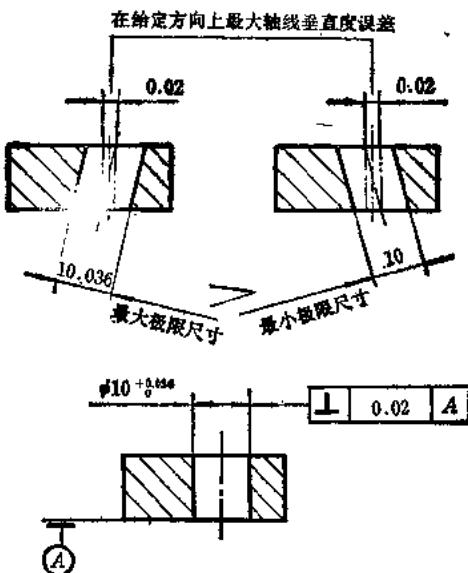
采用独立原则的板孔垂直度公差与尺寸公差无关
